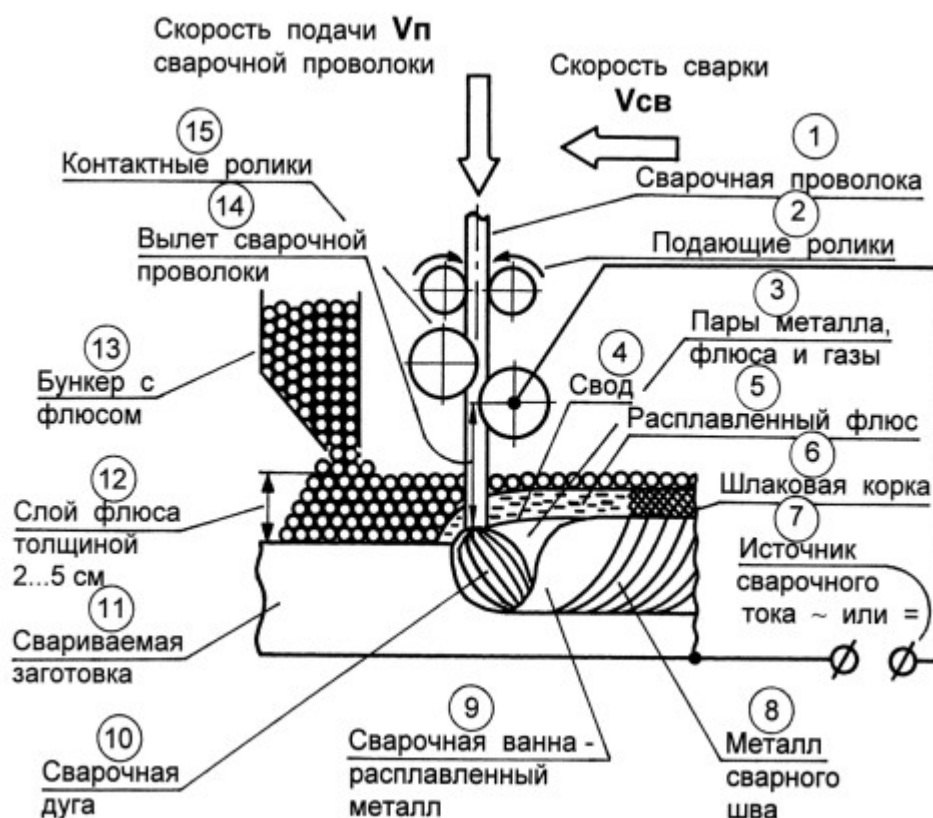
Схема процесса автоматической сварки под флюсом
